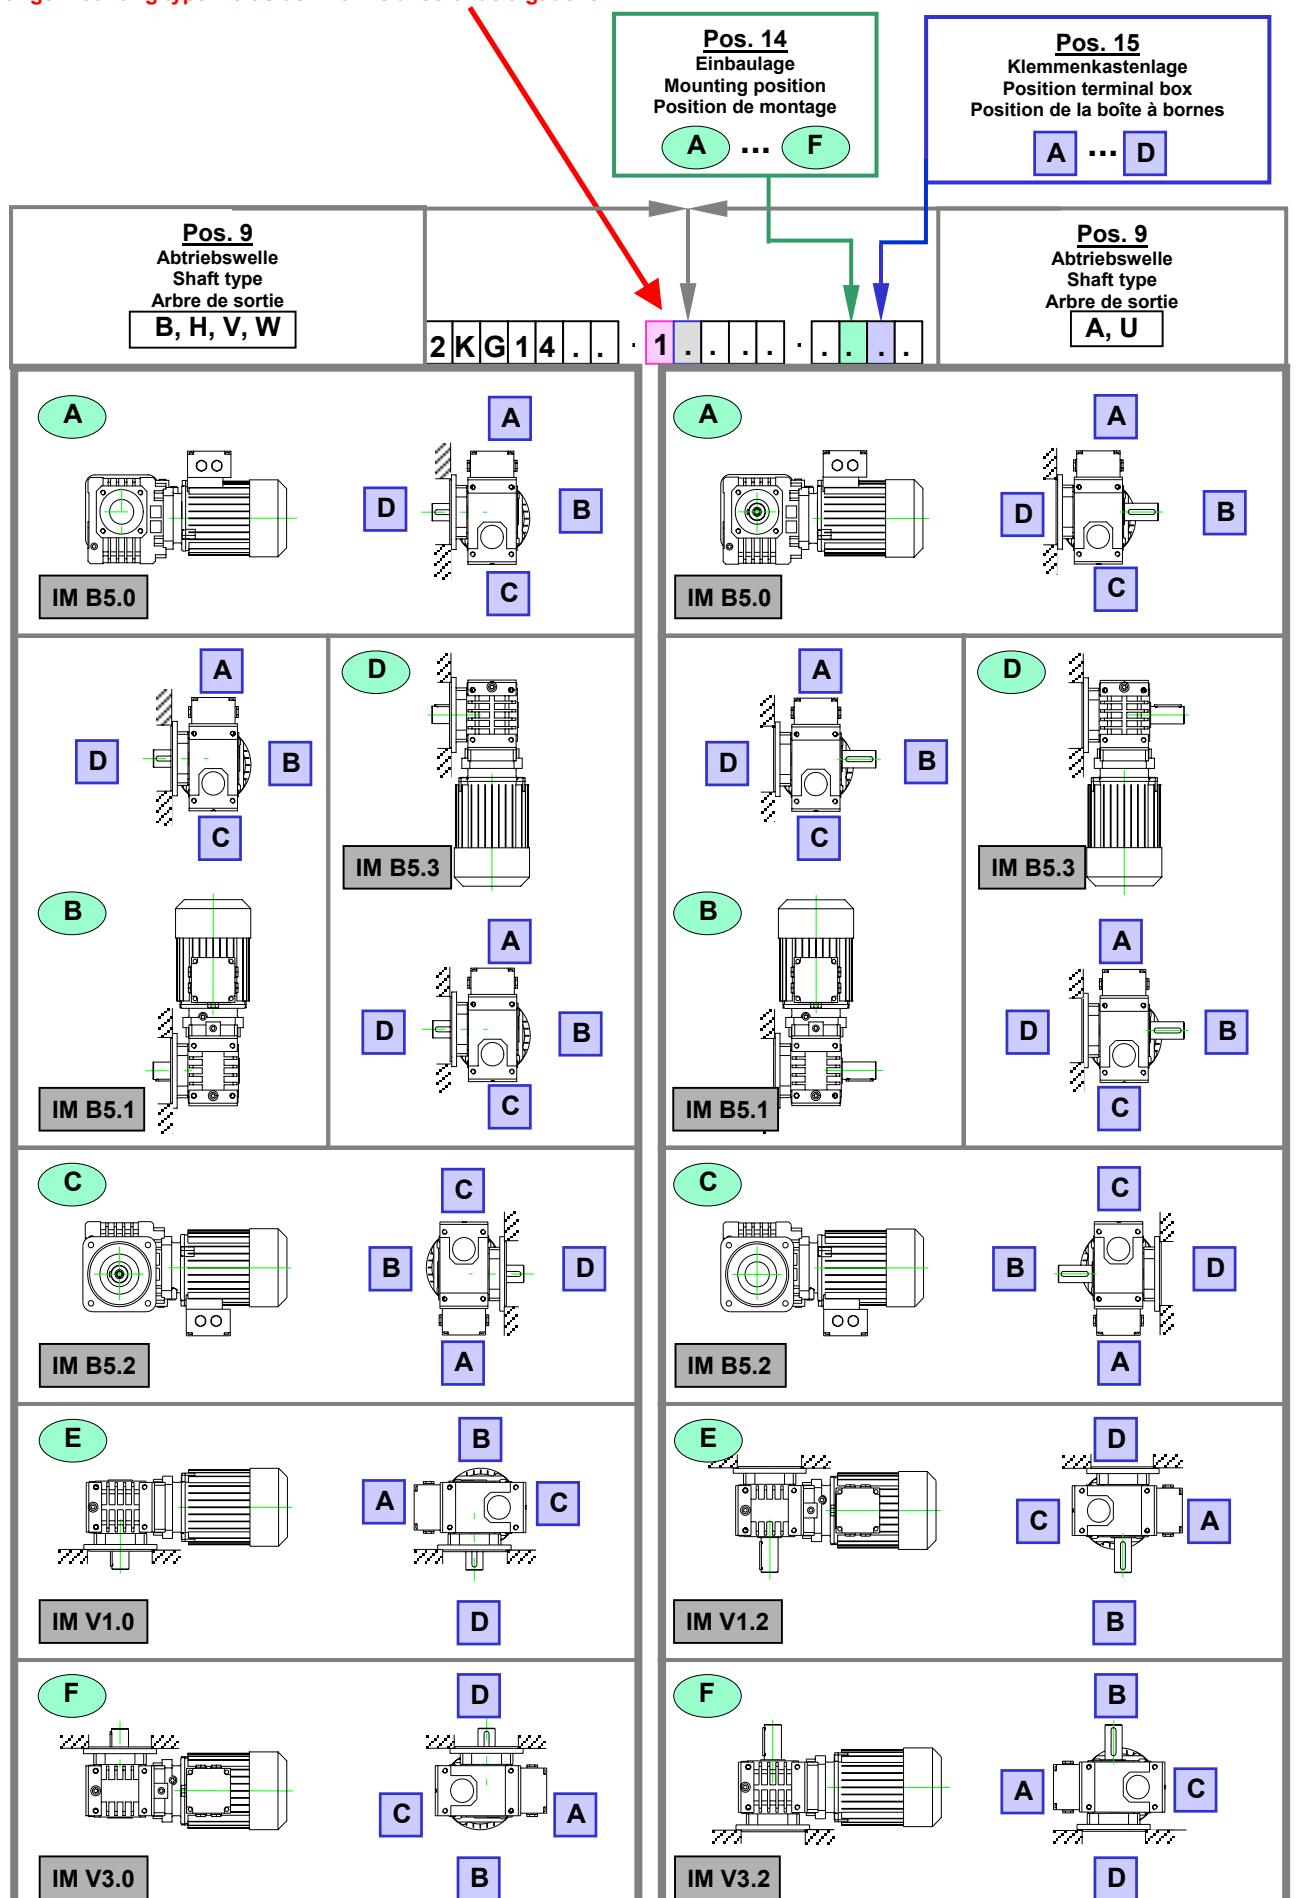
/ Fig. 5 / Tab. 5 Pos. 8 = 6 Bauform / Flansch rechts
